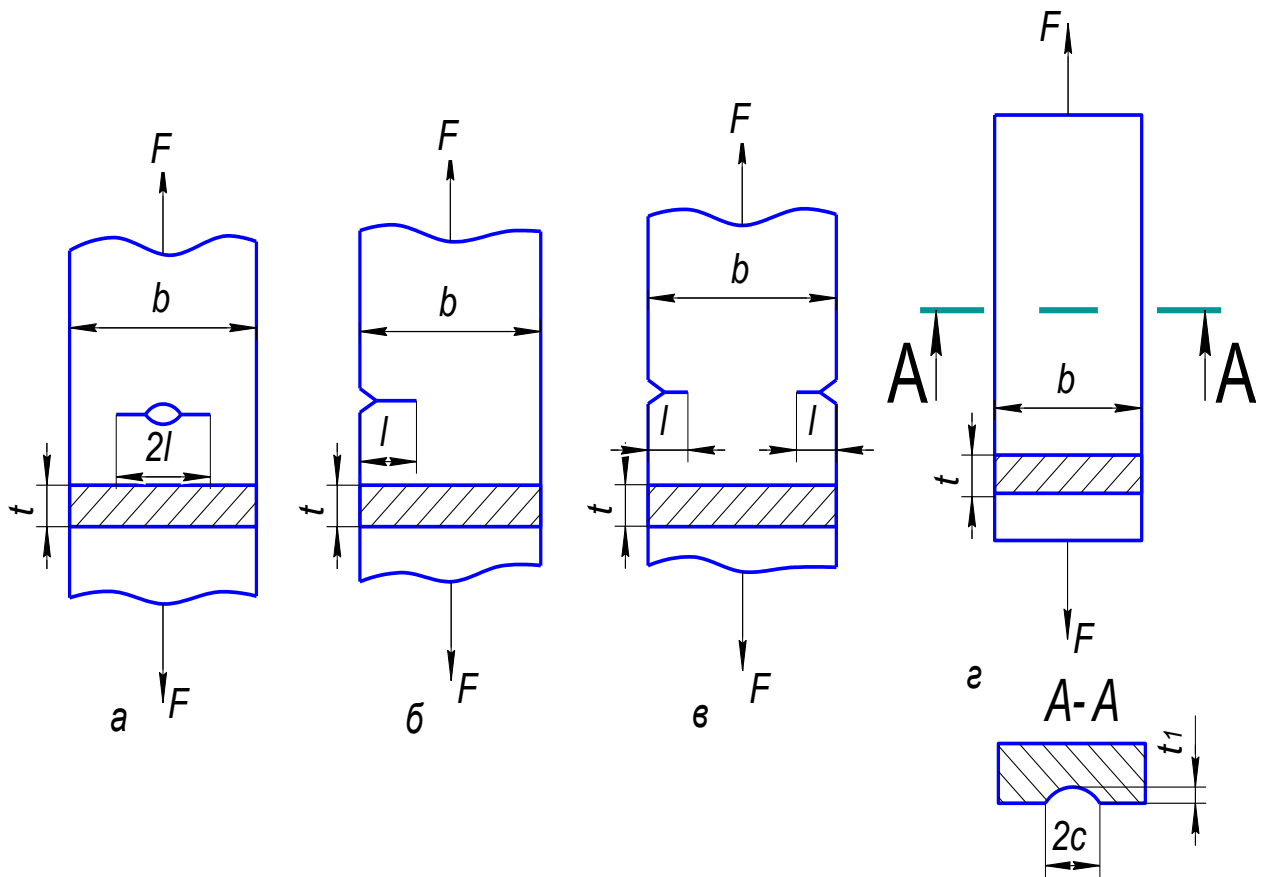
Зразки пластини на розтяг: а) – з центральною тріщиною; б) – з боковою тріщиною; в) – з двома боковими; г) – з поверхневою сегментною.
